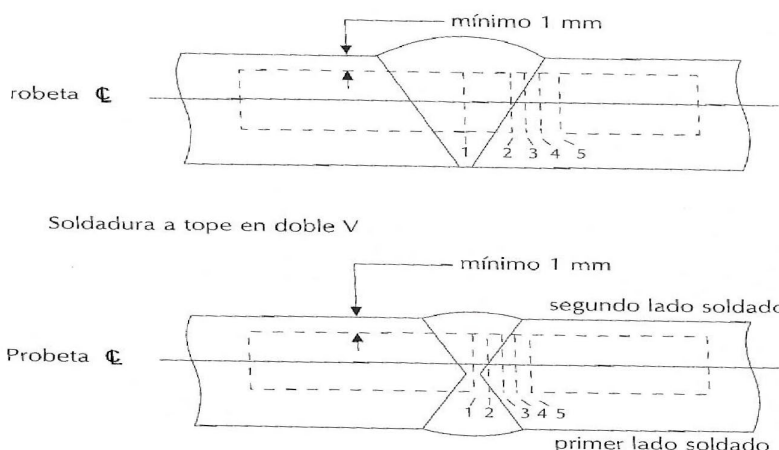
Orientación de la probeta de prueba de soldadura
